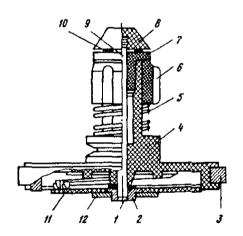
Приемный полкассетный узел: 1— щайба; 2— втулка; 3— кольцо; 4— обойма; 5—пружина; 6— втулка; 7— втулка; 8— фиксирующая кнопка; 9— ось; 10— щайба; 11— плата датчика, 12— шасси
